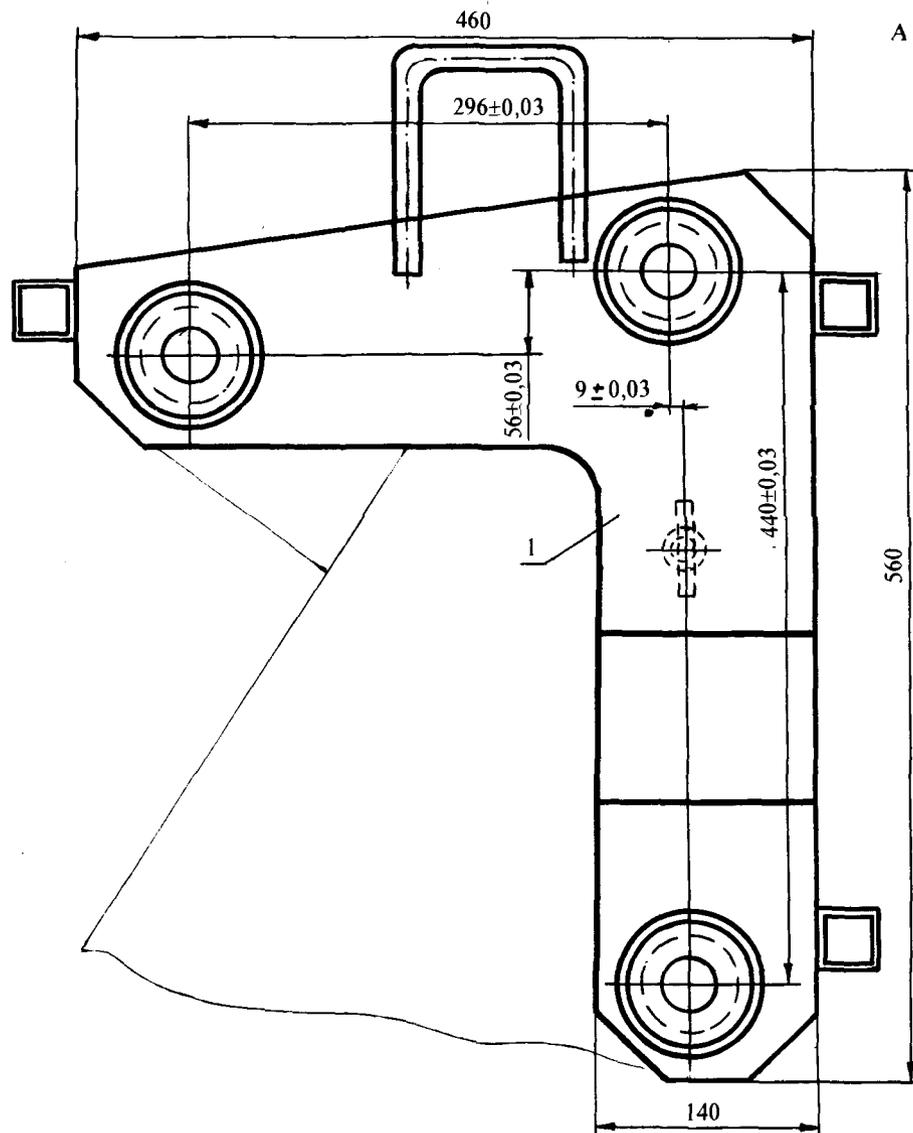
Приспособление для контроля расположения отверстий в рамах (вид А на рис. 4.30):
